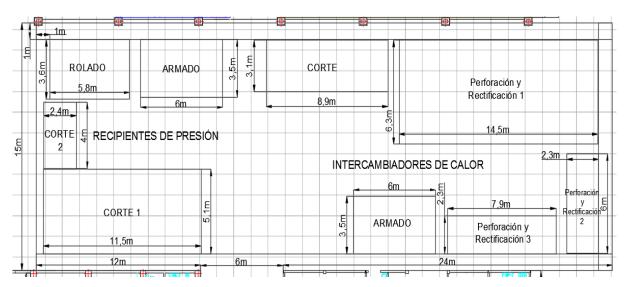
Propuesta de distribución en planta del taller de máquinas y herramientas
